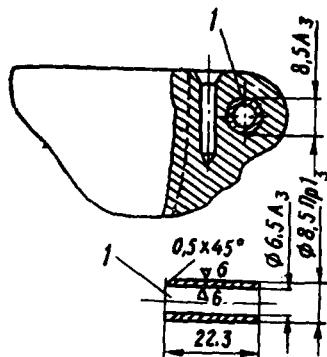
Установка втулок в бо- бышки головок цилиндров:
